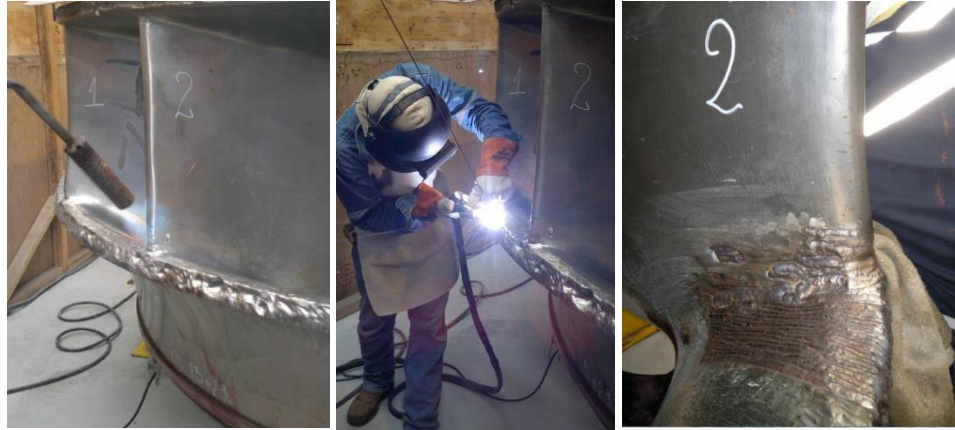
Calentamiento y soldadura de rodete Francis
